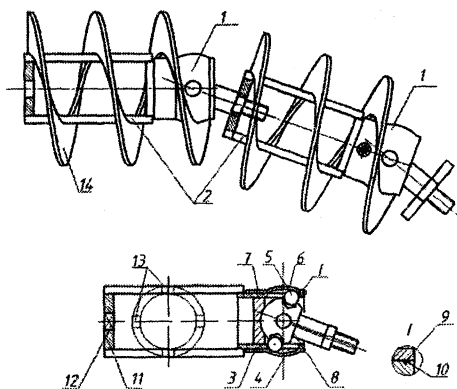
Гвинтовий секційно-шарнірний робочий орган
